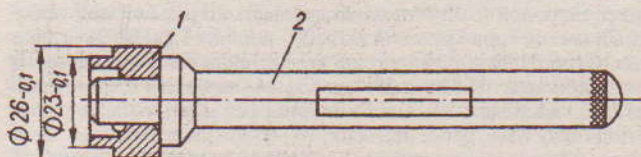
Оправка для выпрессовки втулки вала сошки: 1 - оправка; 2 - ручка
